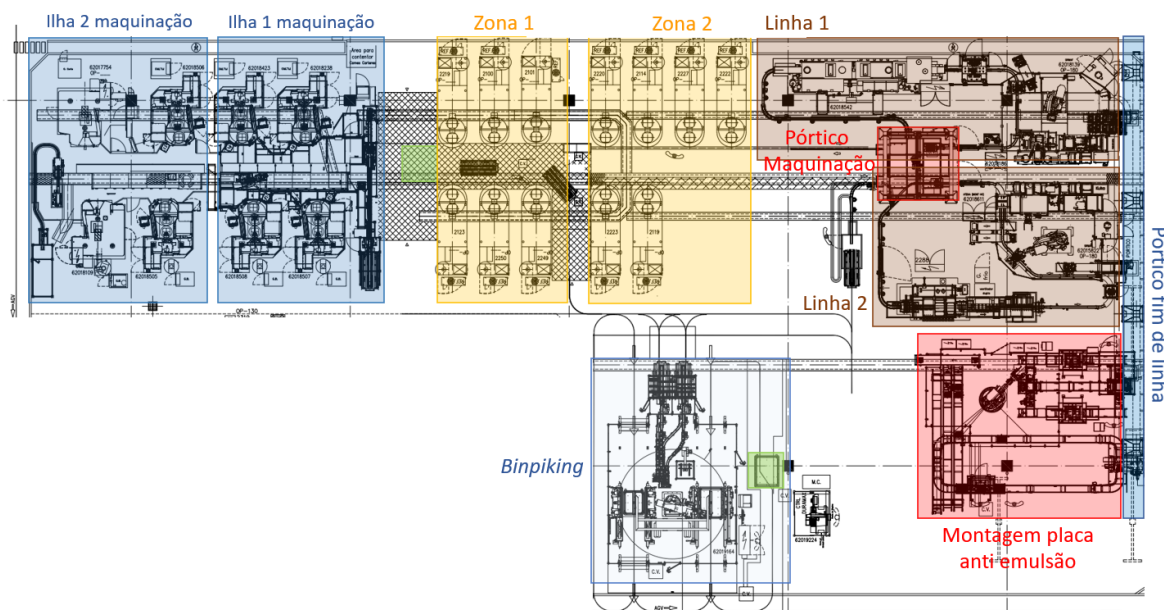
Layout das linhas L1/L2 do cârter intermédio H5.
